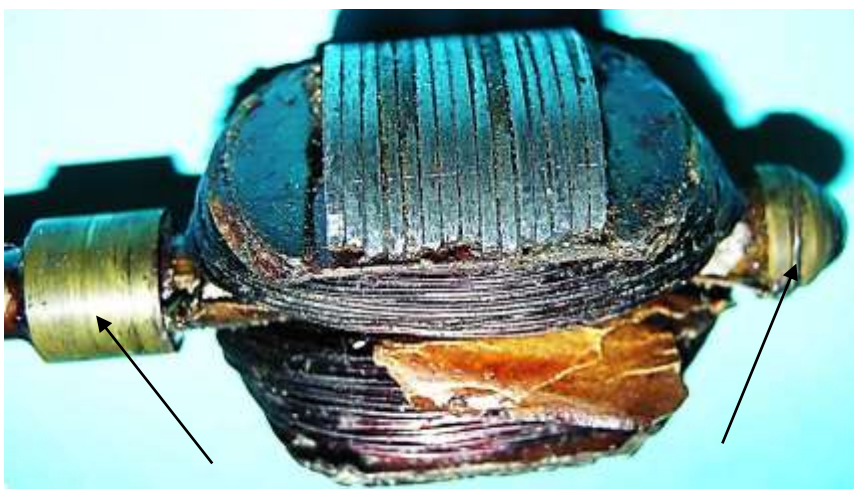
Anschlüsse der Ankerwicklung, Ankerdurchmesser 29 mm, Blechpaketlänge 17 mm
